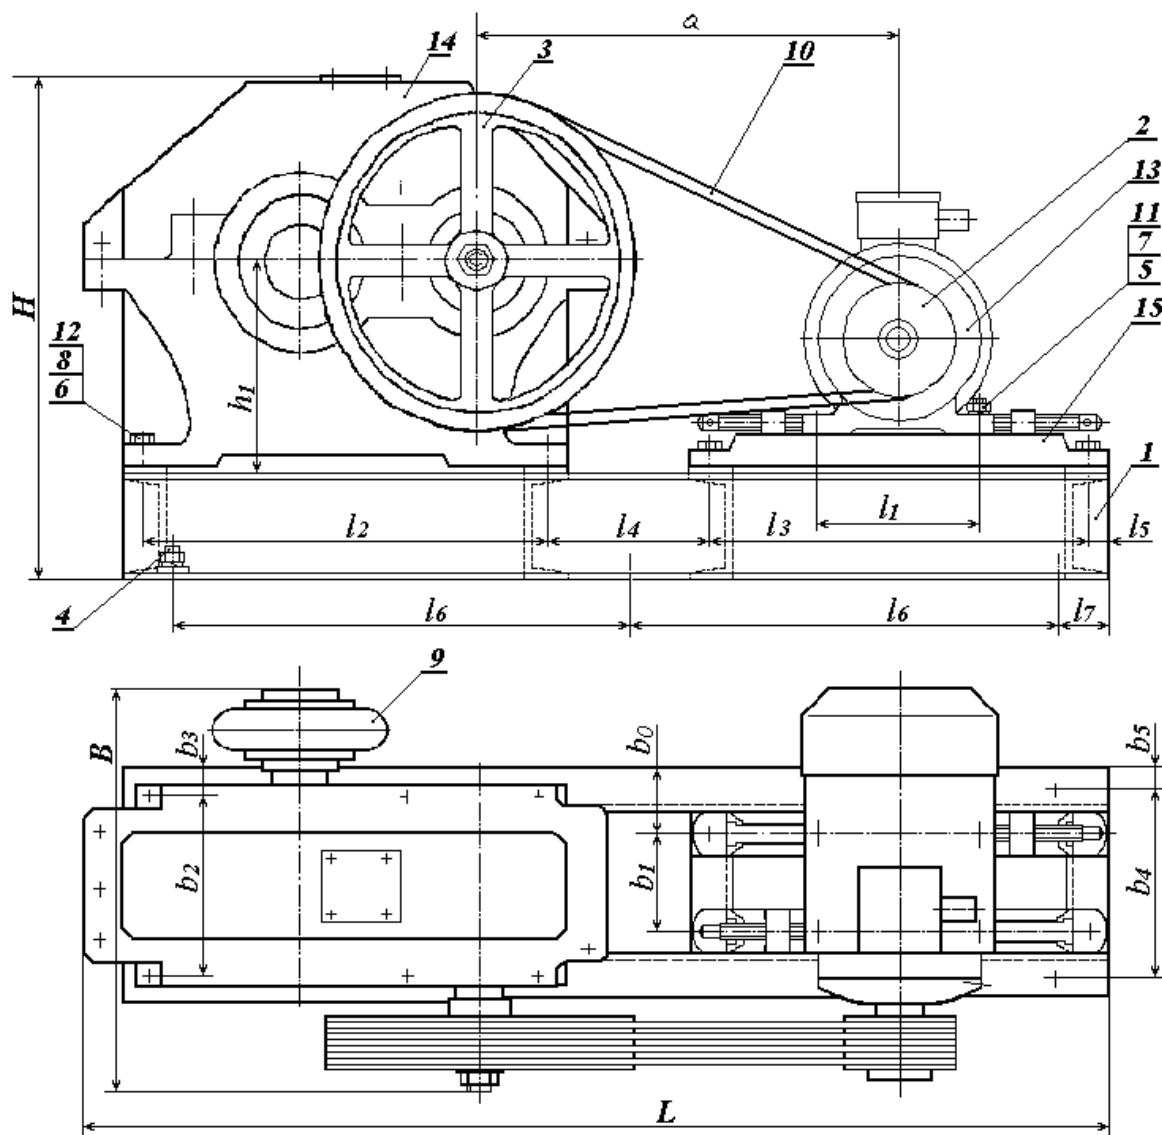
Пример оформления чертежа привода с ременной передачей и редуктором типа 1ЦУ
